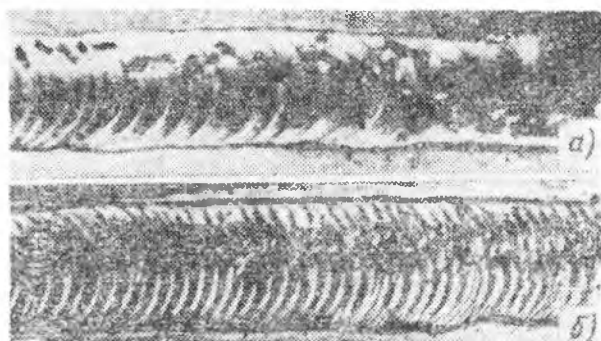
Внешний вид швов, выполненных непрерывной (а) и импульсной (б) сваркой, при расположении анодной пленки до сварки в центральной части торца
